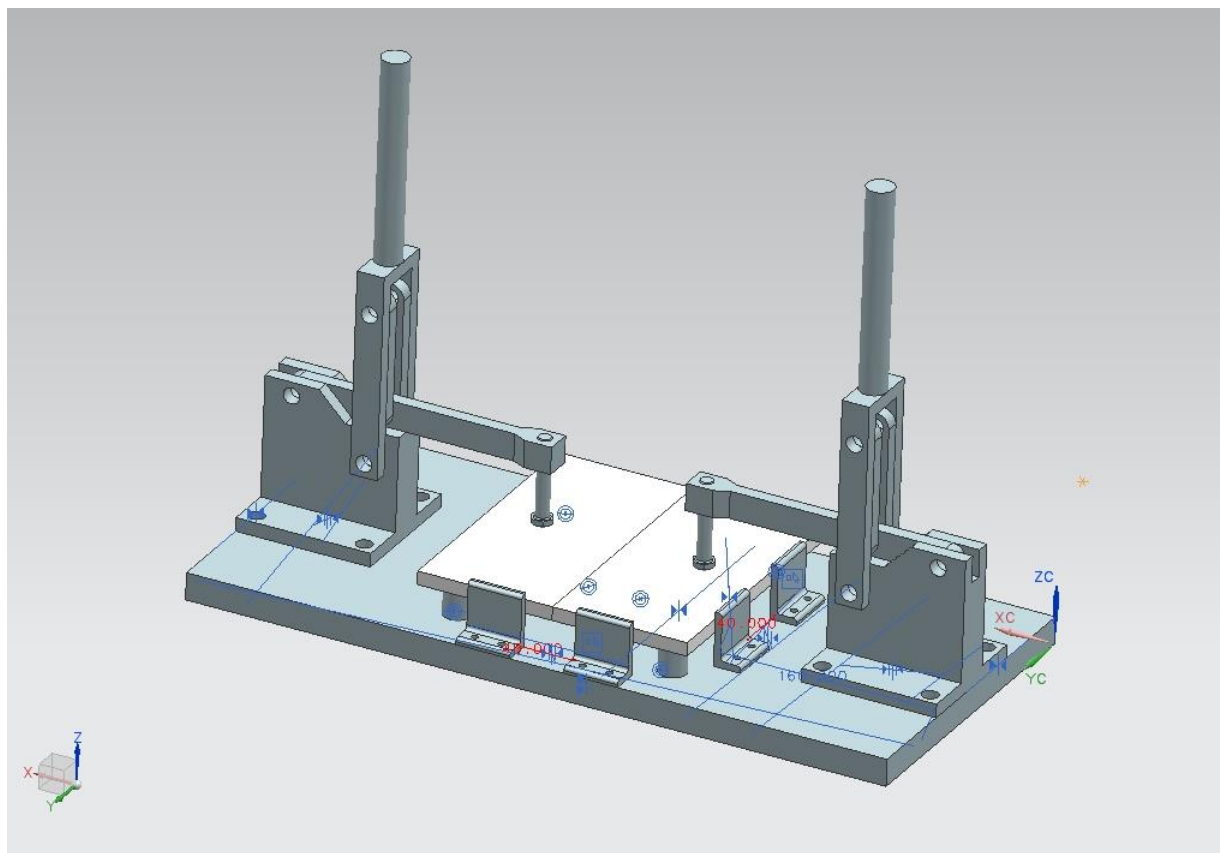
Приспособление для сборки под сварку пластин.
